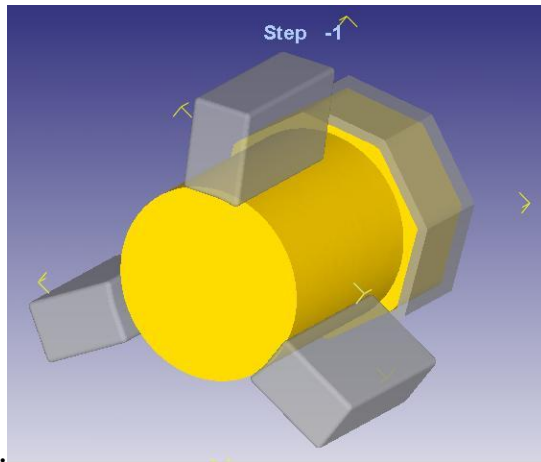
Твердотельная модель устройства для профилирования заднего конца заготовки
